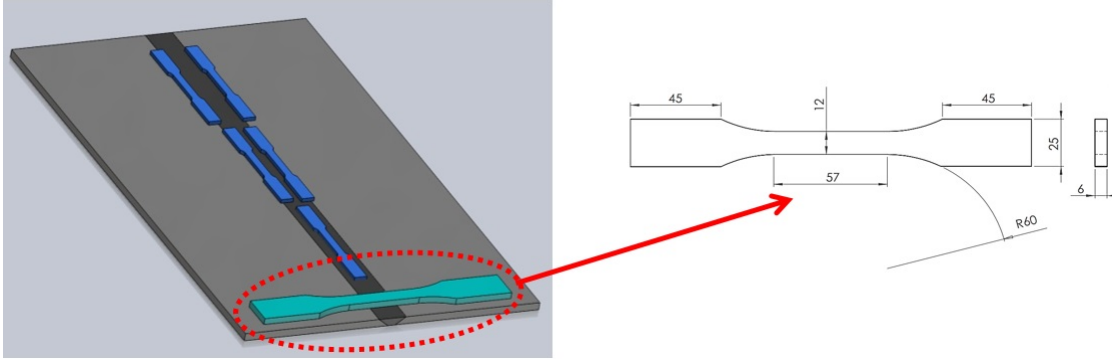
Schéma illustrant le prélèvement des macro-éprouvettes par rapport au joint de soudure.
